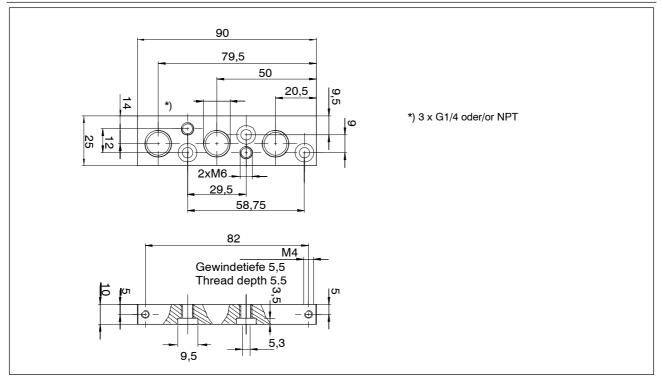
Maßbild Anschlussleiste für KunststoffgehäuseFig. 24Dimension drawing of terminal block for plastic housing
